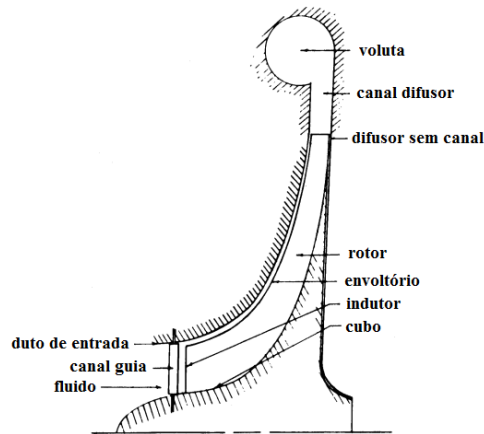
Corte esquemático de um compressor centrífugo [adaptado de Boyce, 2002].
